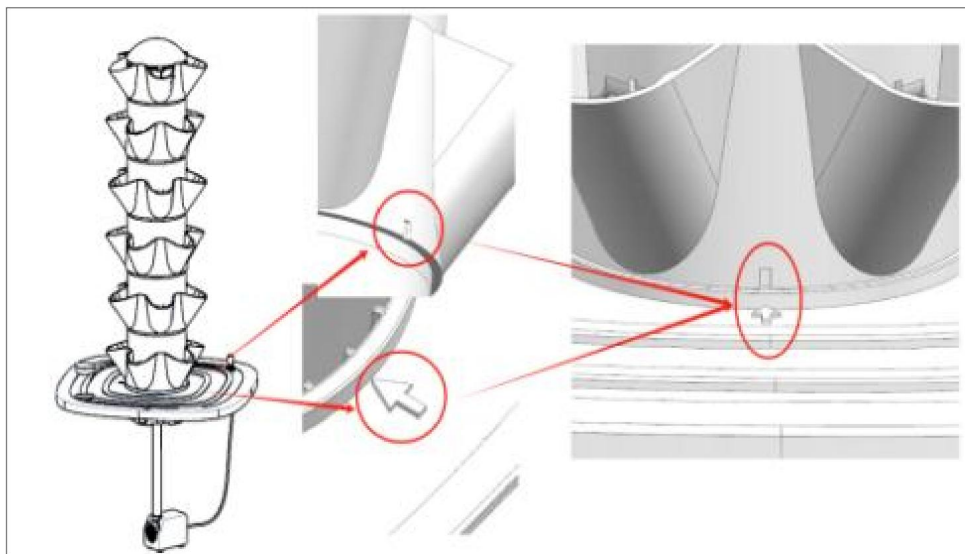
Far passare la pompa dell'acqua attraverso il centro del coperchio del secchio come mostrato, quindi assemblare la torre dell'acqua al coperchio del secchio.
